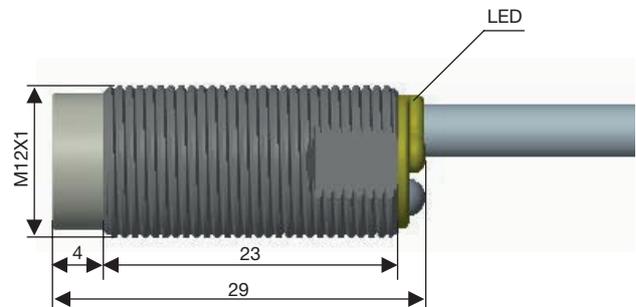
Kurze Ausführung, Nicht bündiger Einbau, Kabel
